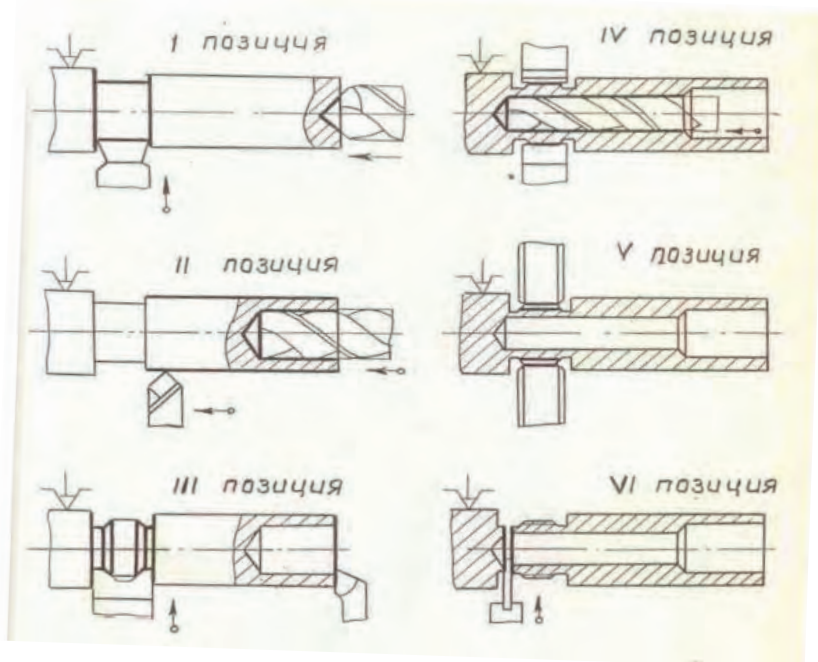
Схема наладки автомата 1Б265 - 6К для обработки корпуса клапана
